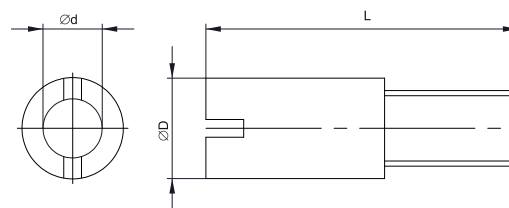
Габаритные размеры разъёма / Figure 1 – Overall dimensions of the connector
